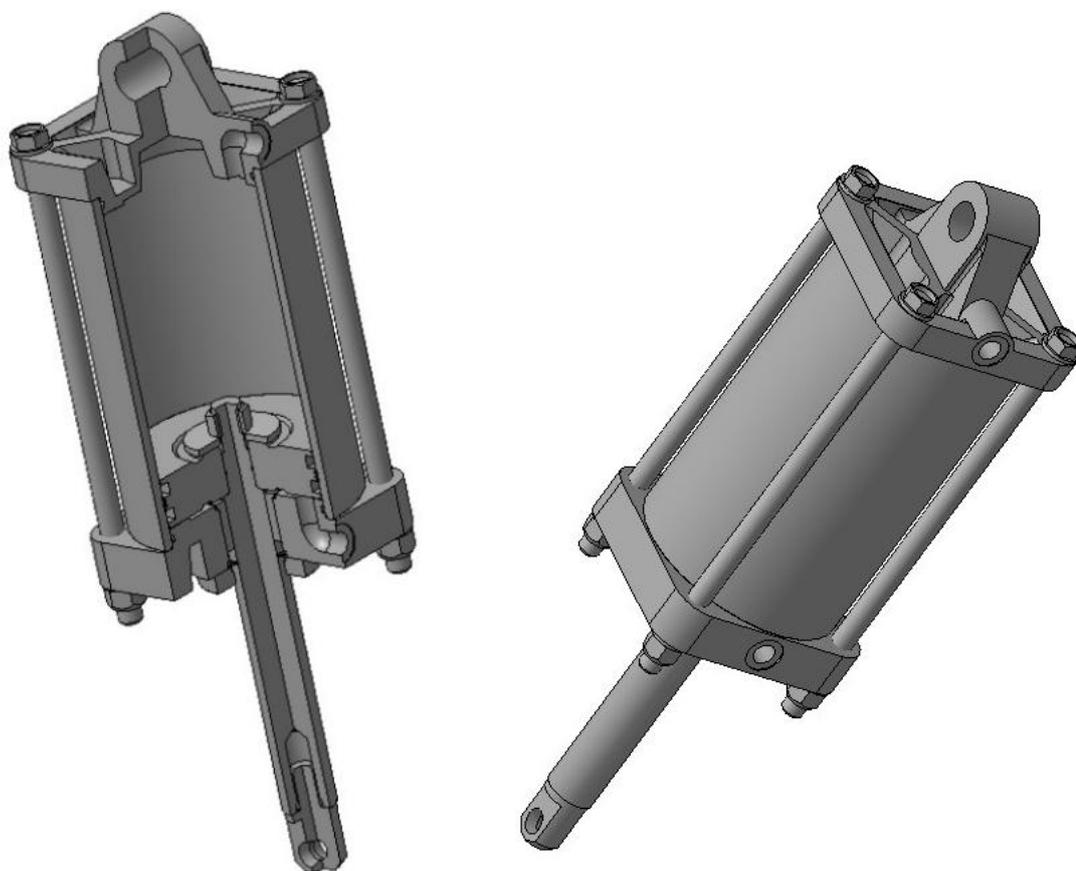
Сборочная 3D-модель узла прессы «Уравновешиватель ползуна»
